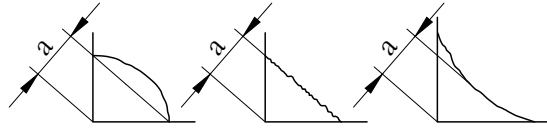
Der maßgebende Querschnitt der Schweißnaht
